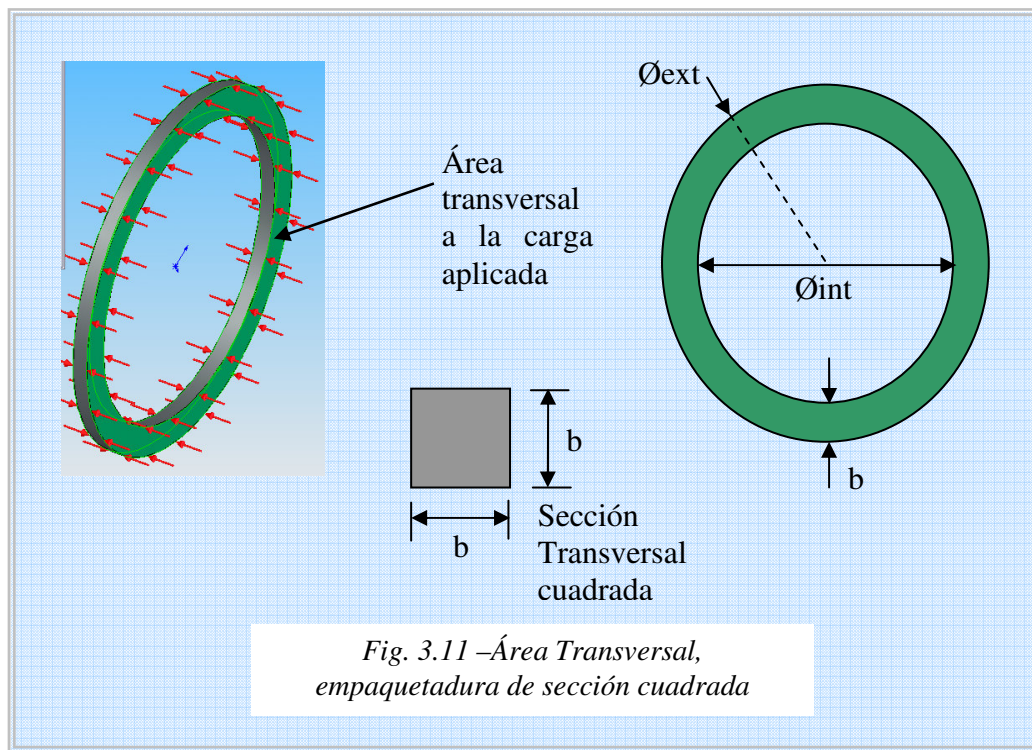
Área Transversal, empaquetadura de sección cuadrada
